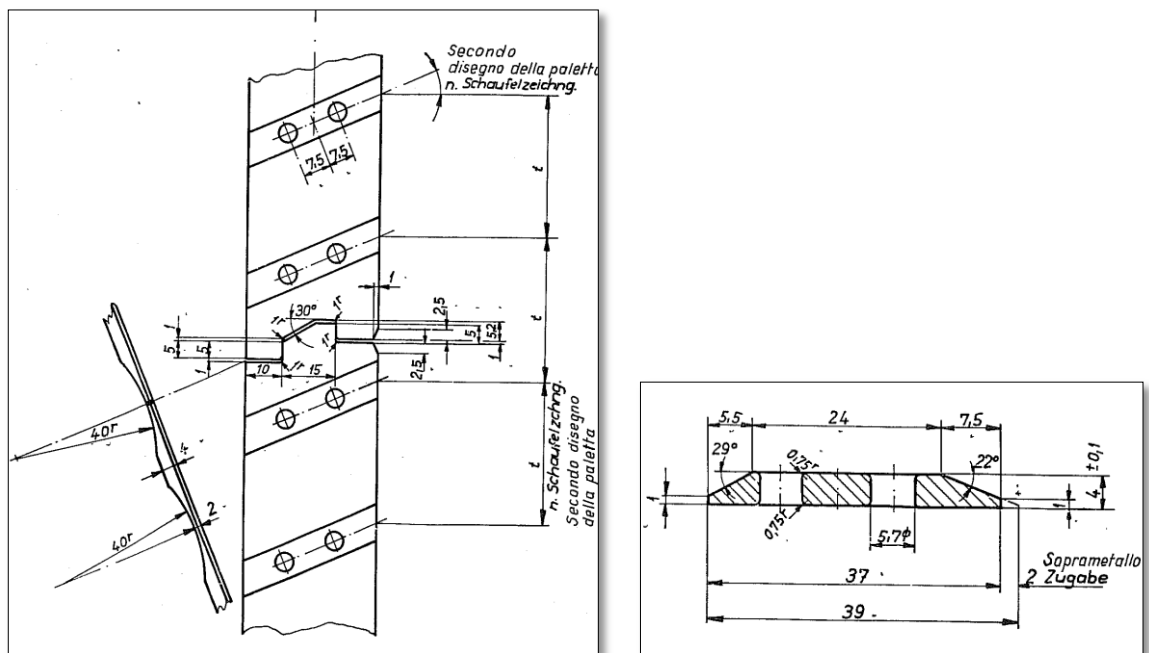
dimensioni del bendaggio del 8° stadio della macchina n° 2.
